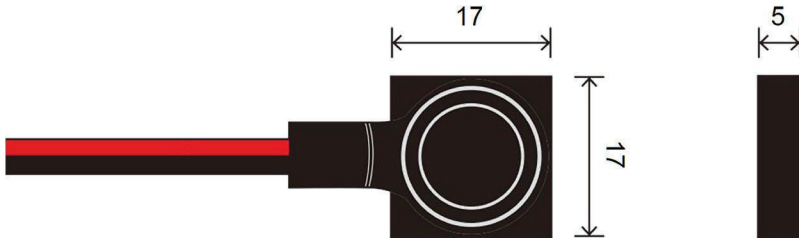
Tutte le dimensioni sono espresse in millimetri
